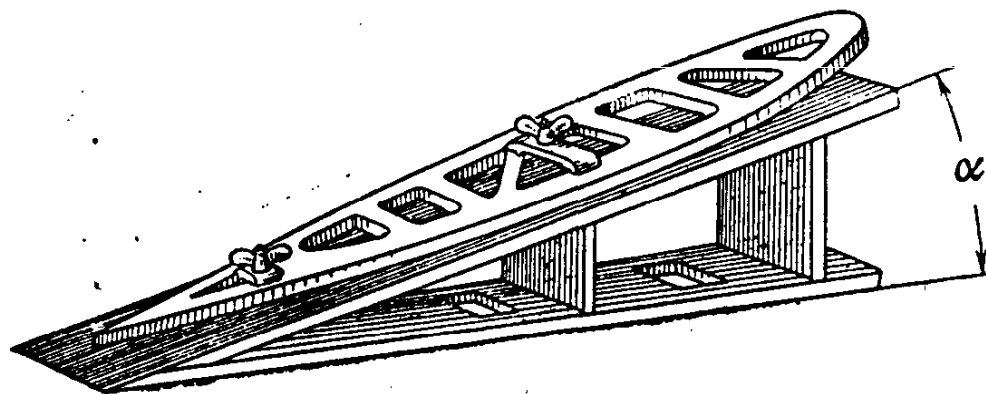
Режущий инструмент для снятия малки нервюр в приспособлении.
